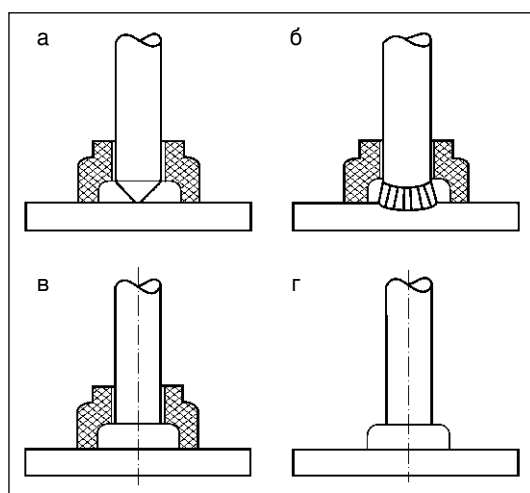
Стадии дугоконтактной сварки стержней в керамических кольцах
